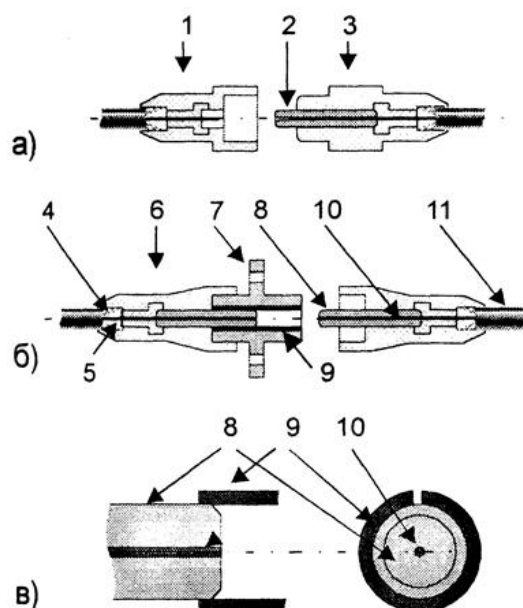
Конструкции соединителей: а) несимметричная; б) симметричная; в) наконечник и центратор розетки симметричного соединителя. Обозначения: 1 - соединитель гнездовой; 2 - наконечник-капилляр; 3 - соединитель штекерный; 4 - кевларовые нити; 5 - эпоксидный наполнитель; 6 - соединитель; 7 - переходная соединительная розетка (адаптер); 8 - оптический наконечник; 9 - центрирующий элемент розетки; 10 -оптическое волокно; 11 – миникабель
